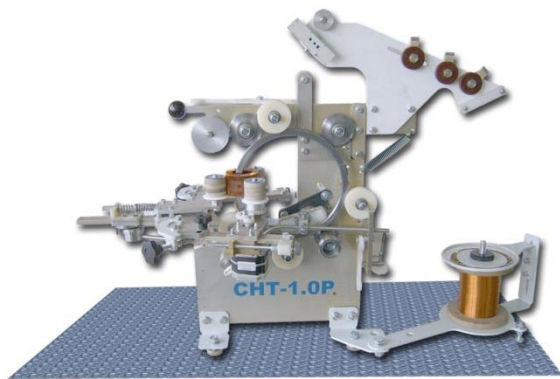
Общий вид станка для тороидальной намотки СНТ-1,0Р
